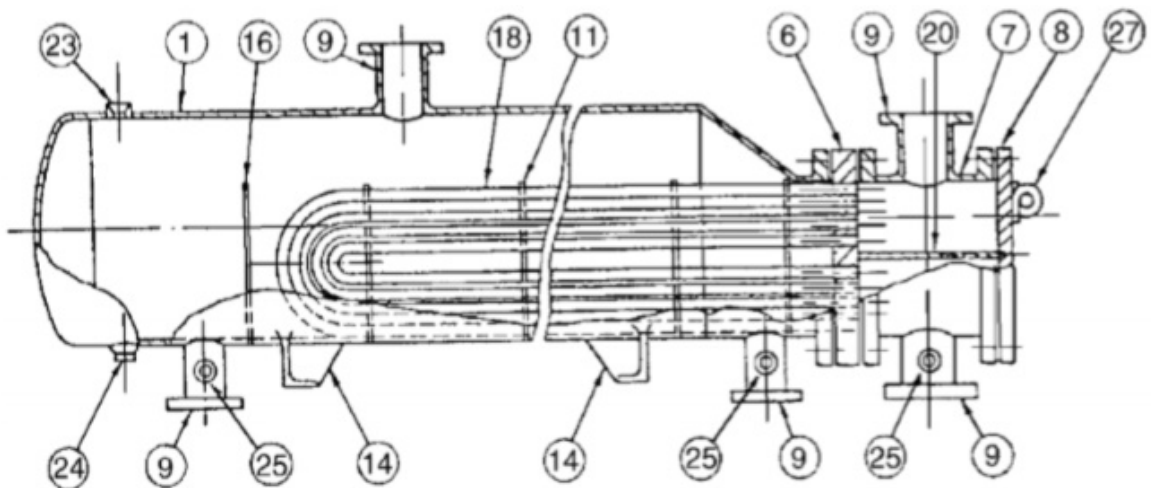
Partes de un intercambiador de calor de carcasa y tubos
